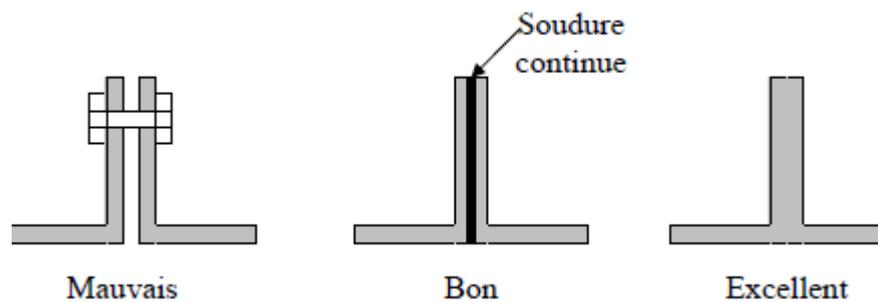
Soudure continue bord à bord préférée aux assemblages rivetés ou boulonnés
